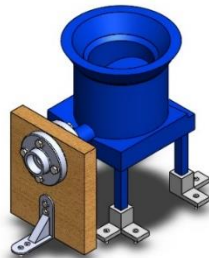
Montaje ensamblado madera de aislamiento. Fuente: Propia.
